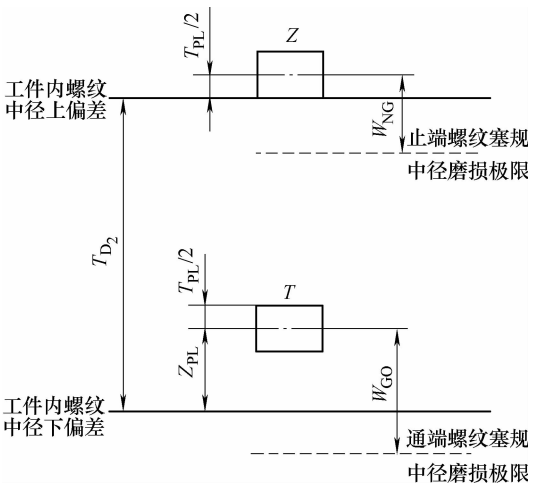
检验工件内螺纹用的螺纹塞规中径公差带图
